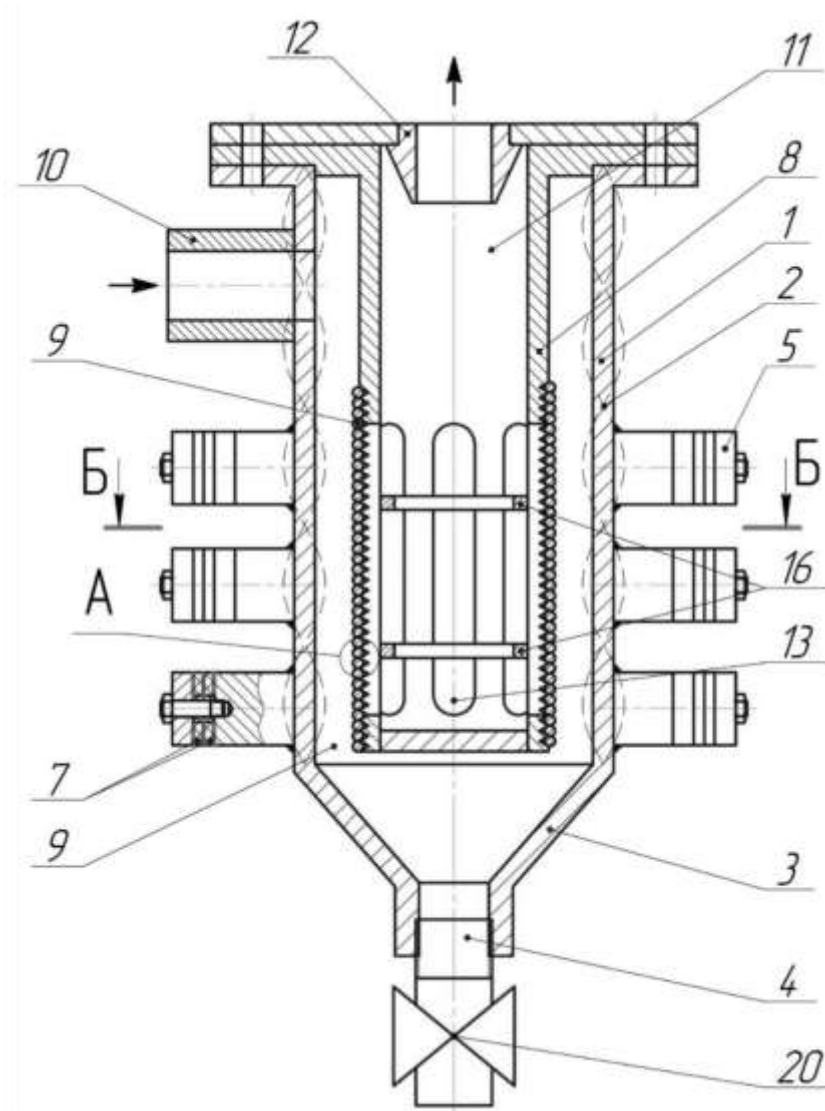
Схема УЗФ з резонансним корпусом
